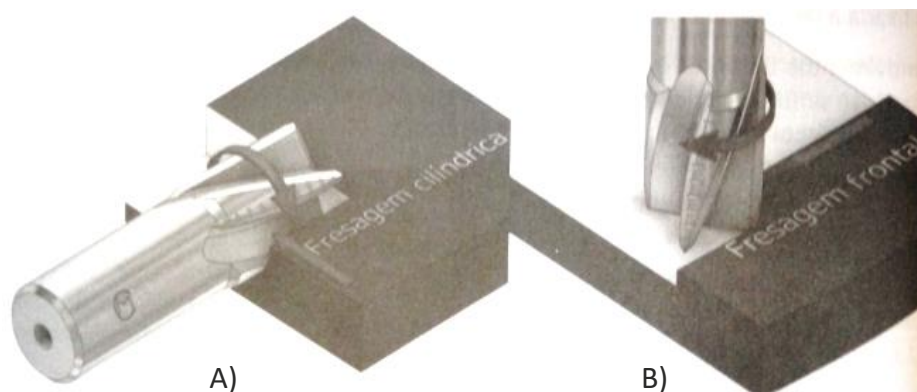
Fresagem cilíndrica e frontal (Rocha, 2016)
